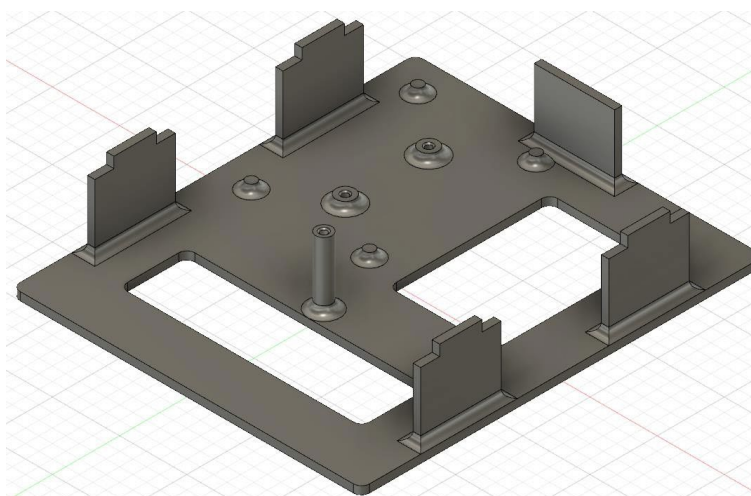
Placă de bază și elemente structurale inferioare (Sursa: Editare proprie)
